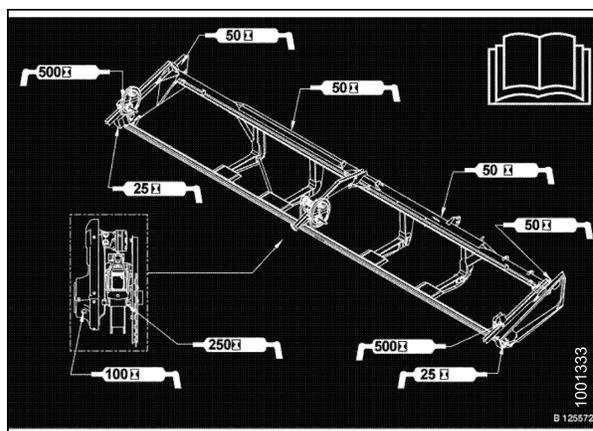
Наклейка с основными точками смазки на жатке с двойным ножом
